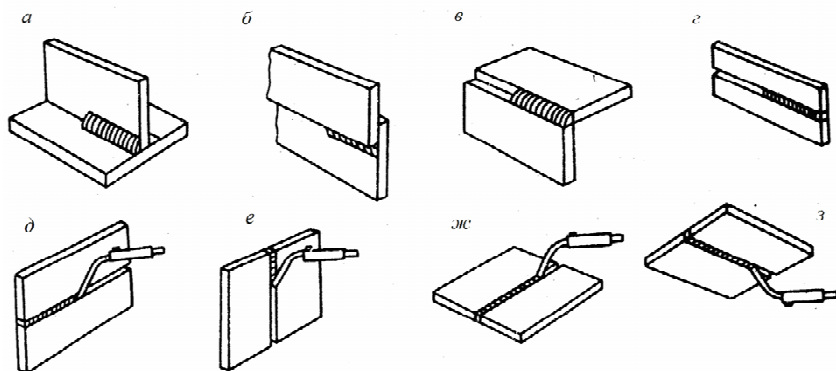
Способы выполнения сварочных швов, их виды:
